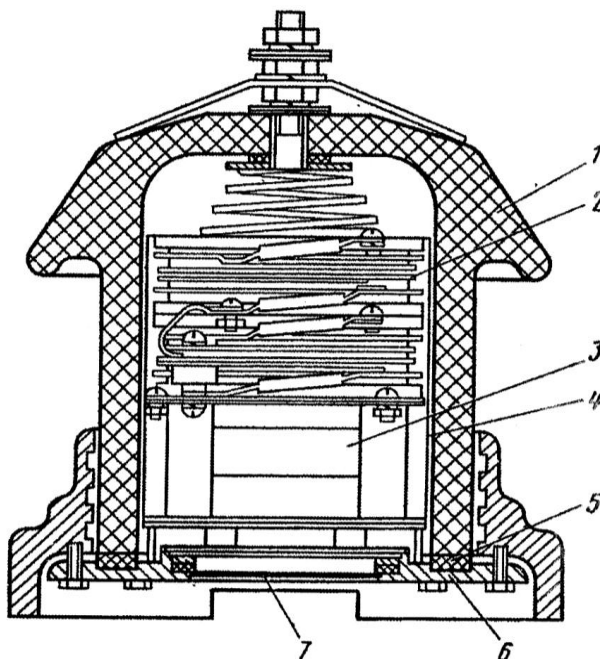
Разрядник РВКУ-3,3А-01: 1 - фарфоровая крышка; 2 - искровой промежуток; 3 - блок нелинейных резисторов; 4 - прокладка; 5 - резиновое уплотнительное кольцо; 6 - днище; 7 - клапан
